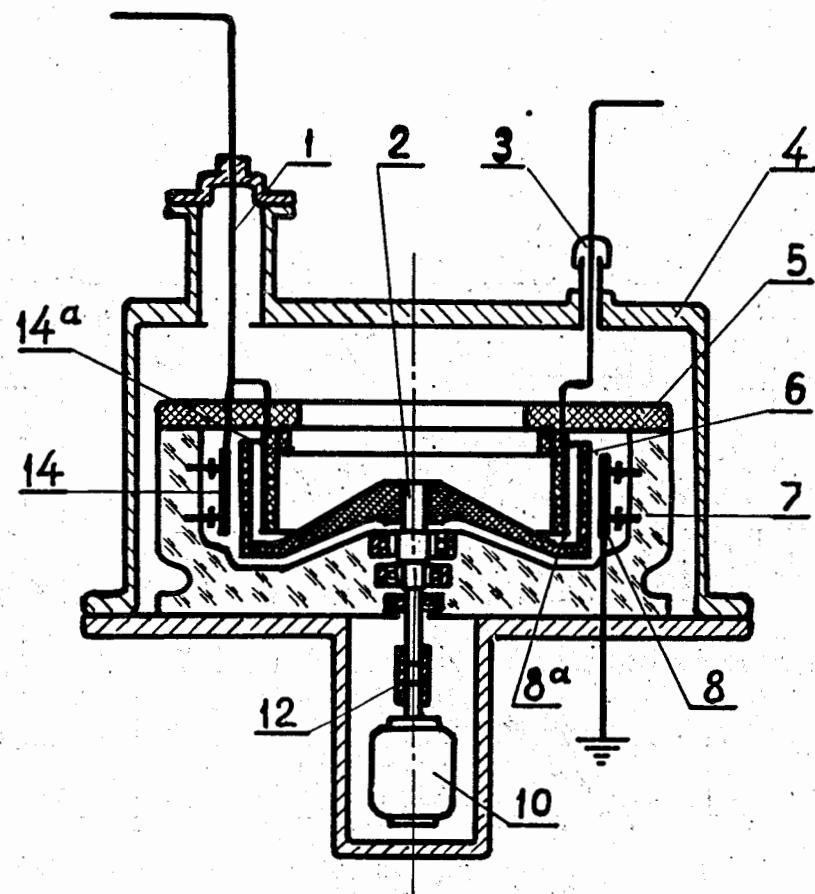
Конструктивные элементы модели РЭГ-Ц-300. 1 - кабельный вывод высокого напряжения; 2 - стальной вал; 3 - ввод напряжения возбуждения; 4 - металлический бак; 5 - статор; 6 - цилиндрический ротор; 7 - станина генератора; 8 - ионизатор возбуждения; 8а - индуктор возбуждения; 10 - электродвигатель; 12 - эластичная муфта; 14 - разрядный ионизатор; 14а - разрядный индуктор.
